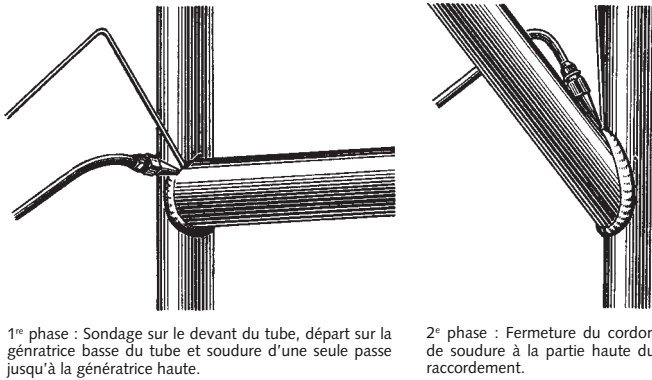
Soudure au chalumeau oxyacétylénique
